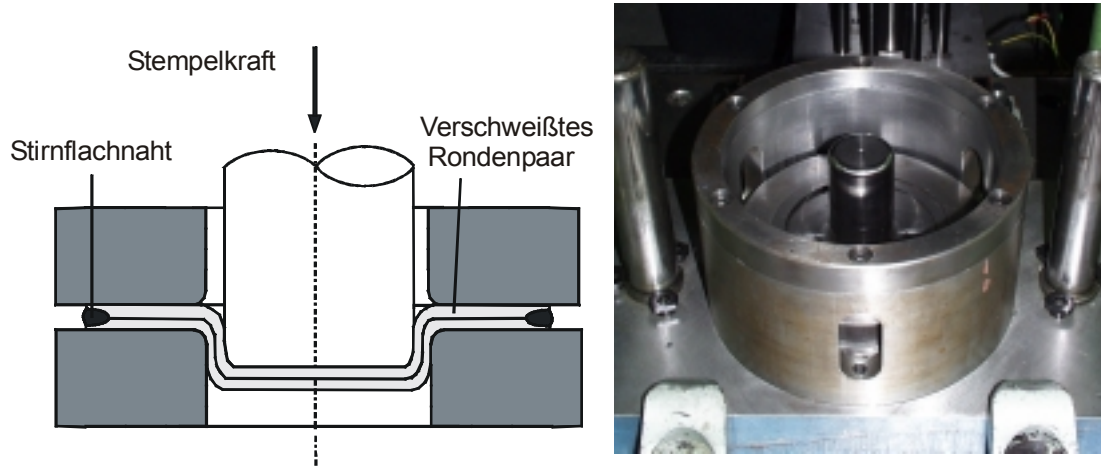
Tiefziehwerkzeug für Napfziehversuch
